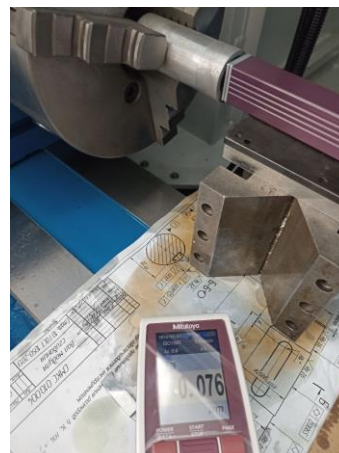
Измерение шероховатости поверхности обрабатываемой детали из материала марки В95
